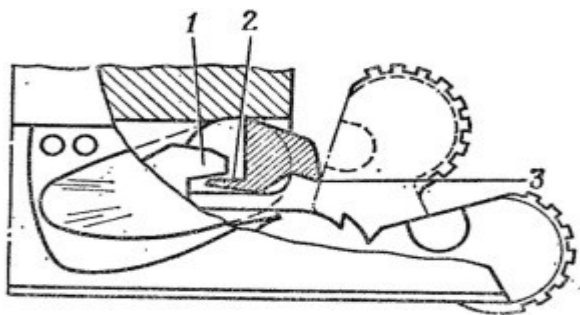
Схема блокировки курка выступом предохранителя: 1 – зуб щептала; 2 – полочка уступа предохранителя; 3 – выступ предохранителя
